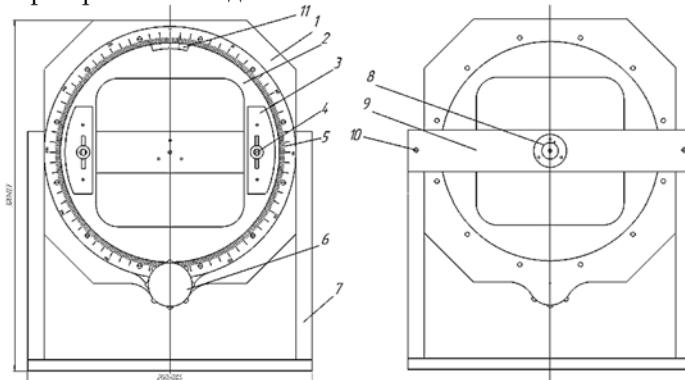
Чертеж общего вида задатчика угловых положений. Вид спереди, сзади: 1 – неподвижное кольцо; 2 – поворотное кольцо; 3 – прижимная планка; 4 – винт-баращек; 5 – шкала; 6 – ручка; 7 – основание; 8 – муфта; 9 – планка; 10 – винт; 11 – нониус
